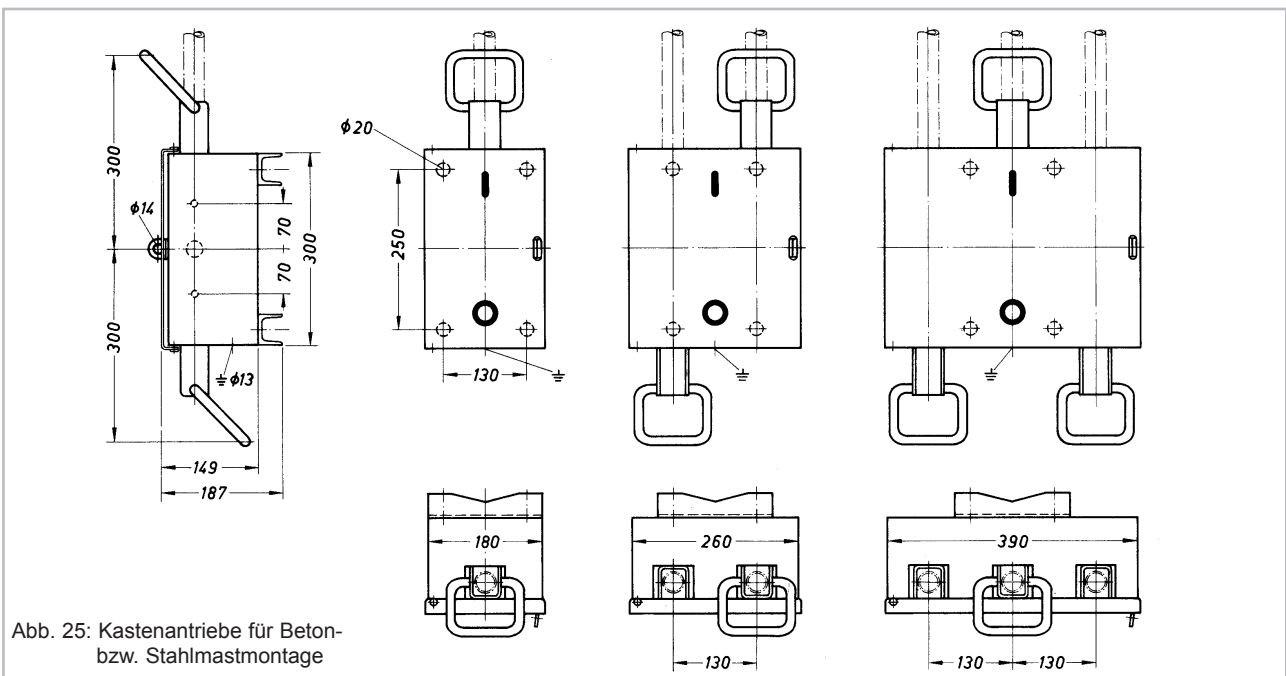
Kastenantriebe für Beton- bzw. Stahlmastmontage
